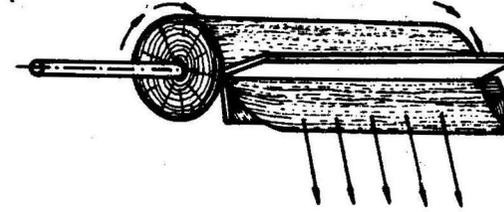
Esquema del principio de trabajo de la máquina chapadora
